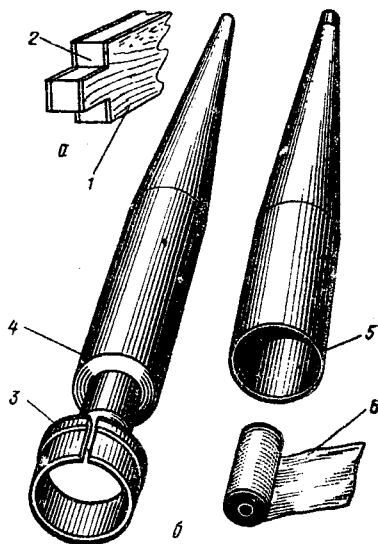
Усиление центральной нервюры и изготовление стеклопластикового фюзеляжа:
